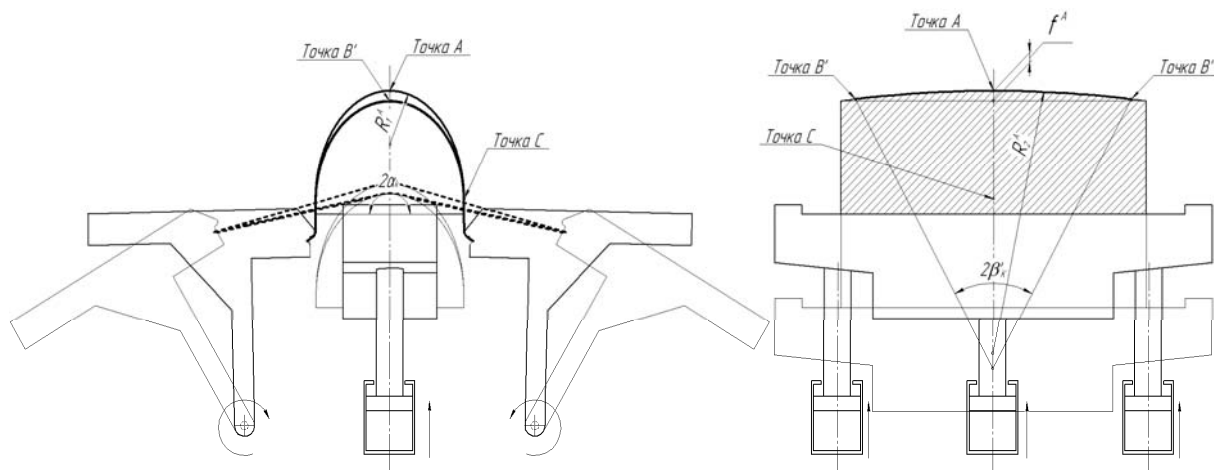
Схема разгрузки и изгибания на прессе FEKD 550-1100 оболочки с полным охватом обтяжного пуансона: 1 - листовая заготовка; 2 - обтяжной пуансон; 3 - рабочий стол прессы; 4 - балансиры; 5 - силовые гидроцилиндры стола прессы
